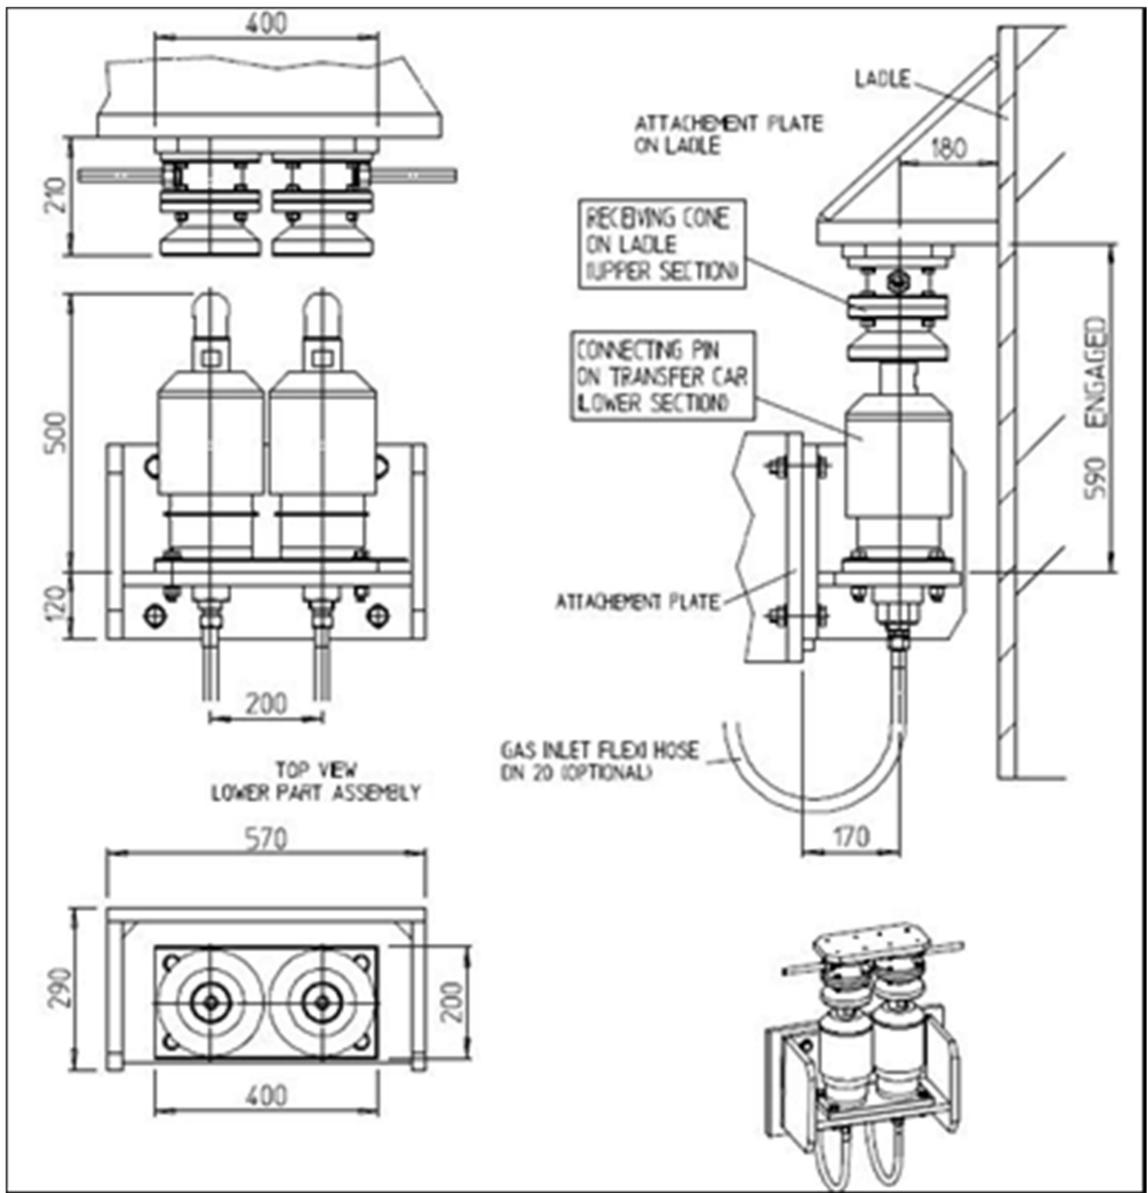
Plano de Detalles de Sistema de Acoplamiento Dual.
